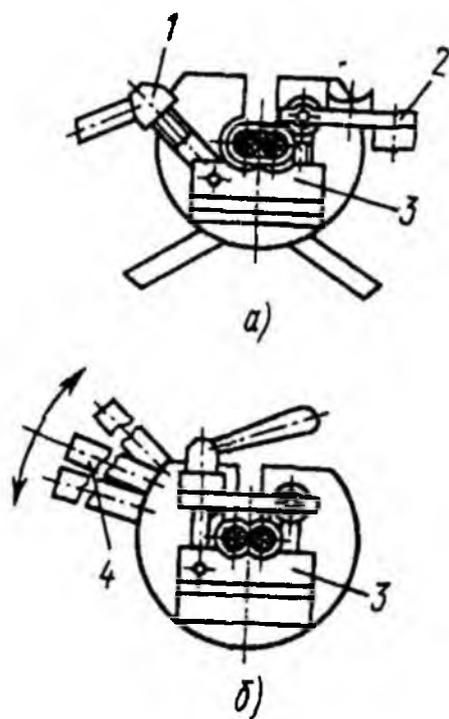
Заушные узлы приспособления МИ-189А:
